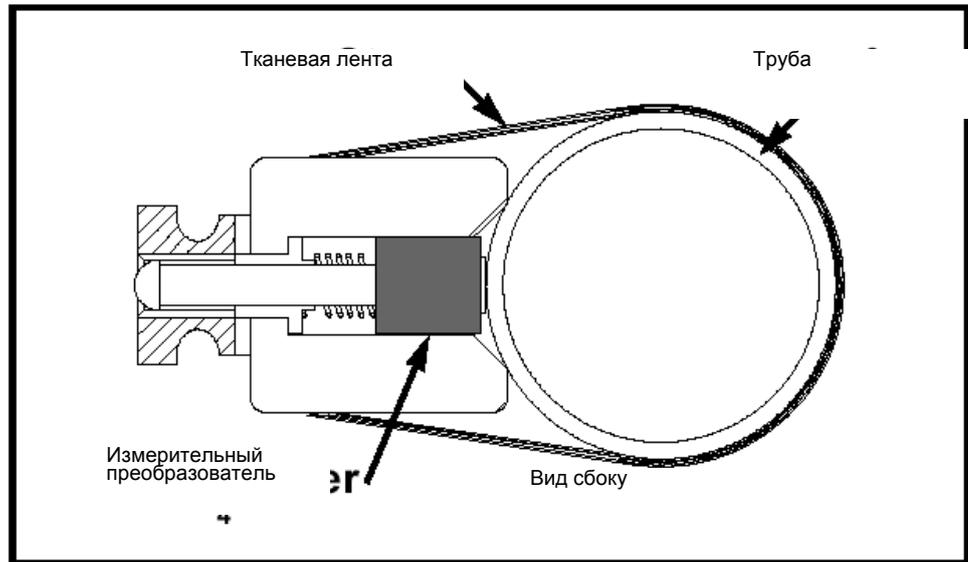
Установка зажимного приспособления для труб небольшого диаметра:
